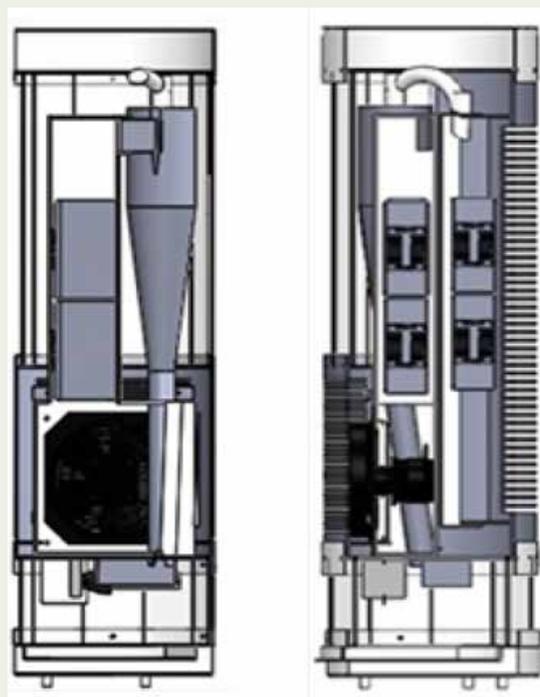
Vista esquemática del dispositivo, a) Vista posterior, b) Vista lateral.
